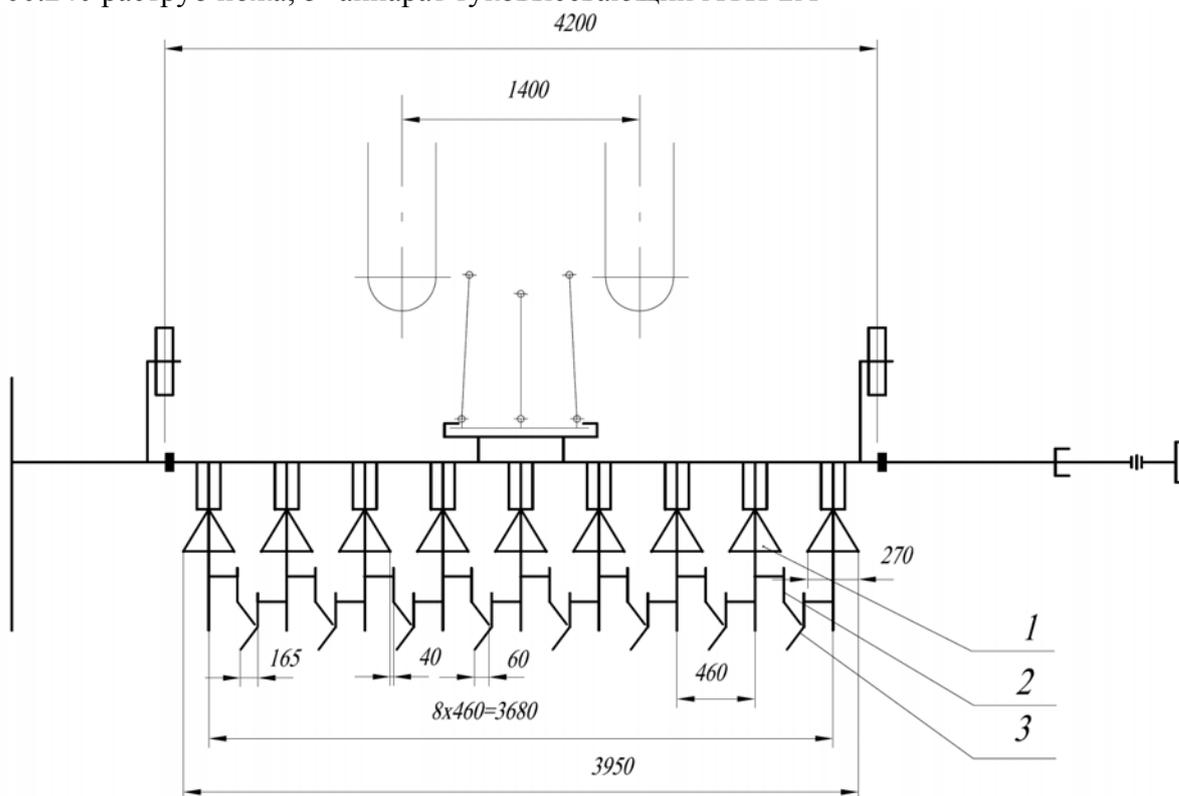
Схема расположения рабочих органов культиватора КРН-5,6К-02 для сплошной обработки почвы
